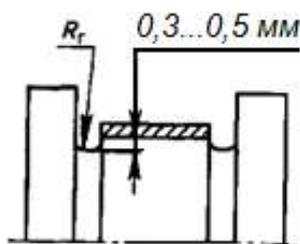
Схема наплавки шеек вала с углублением и упрочнением галтелей
